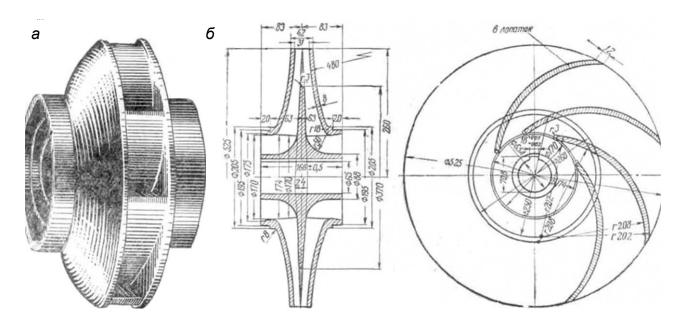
Рабочее колесо насоса типа Д: a — общий вид; б — поперечный и продольный разрезы рабочего колеса
